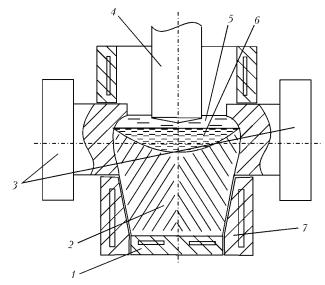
Схема ЭШЛП заготовки корпуса фланцевой задвижки: t- поддон; 2- литая часть заготовки корпуса; 3- приплавляемые патрубки; 4- расходуемый электрод; 5- шлаковая ванна; 6- металлическая ванна; 7- разборный кристаллизатор
